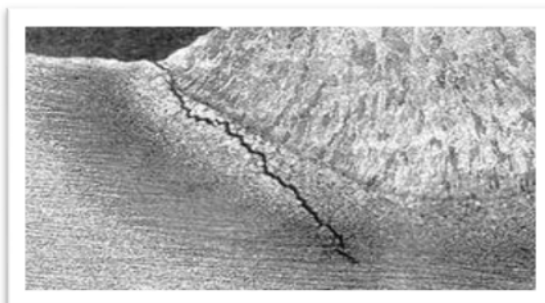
Fissuration à froid. [10]
